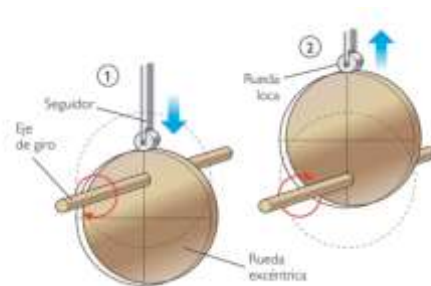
Mecanismo de Excéntrica y Seguidor.
